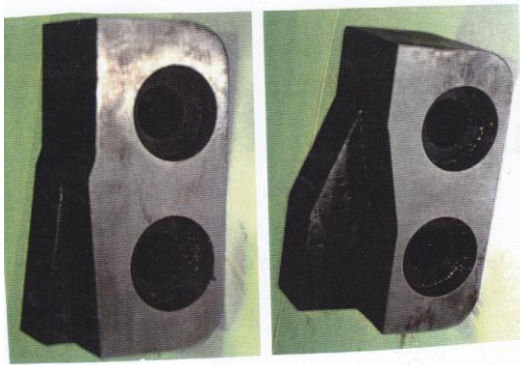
Конструкции ножей с углами наклона режущих и прижимных кромок 5° (а) и 17° 40' (б)
